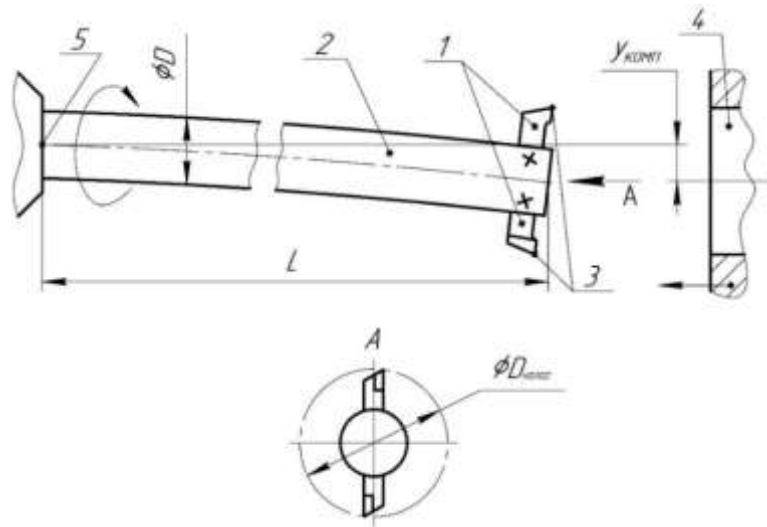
Схема оброблення отвору на горизонтально-розточувальному верстаті: 1 – інструмент; 2 – розточувальна оправка; 3 – вершина інструменту; 4 – оброблюваний отвір; 5 – вісь шпинделя
